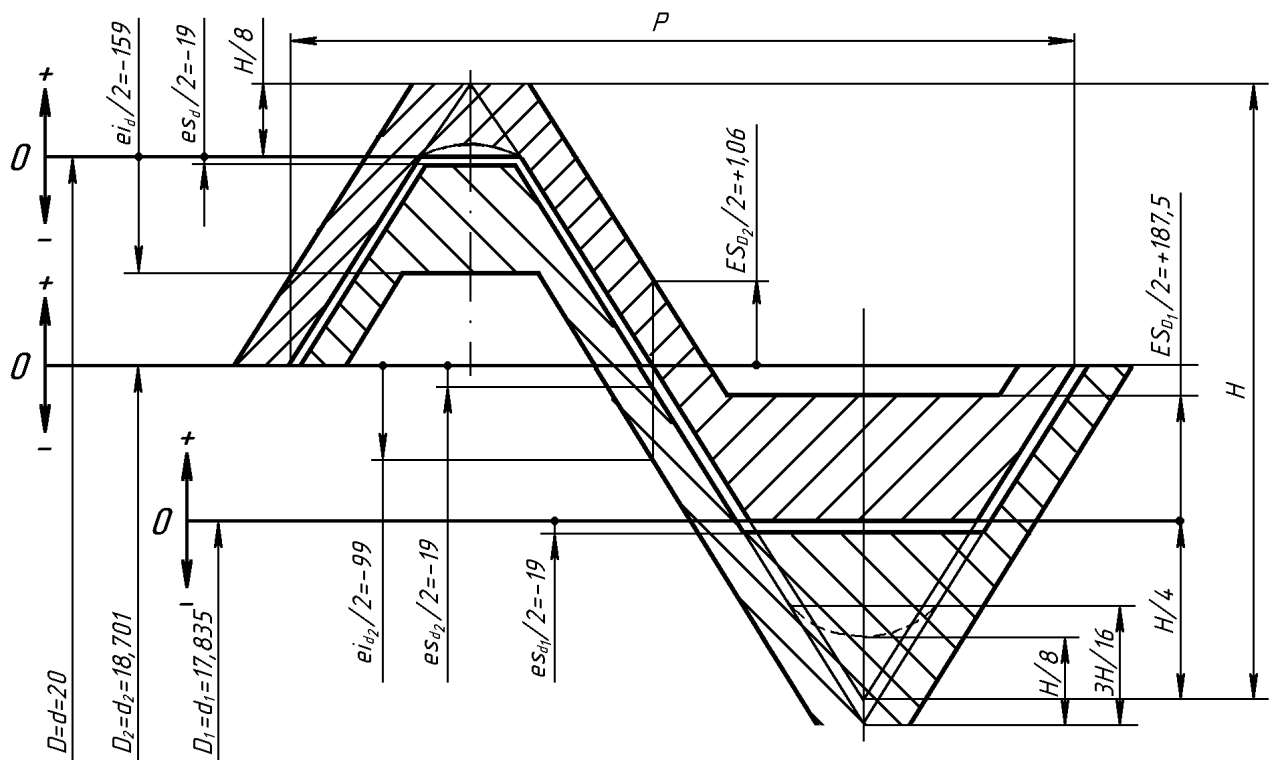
Схема расположения полей допусков резьбового соединения
